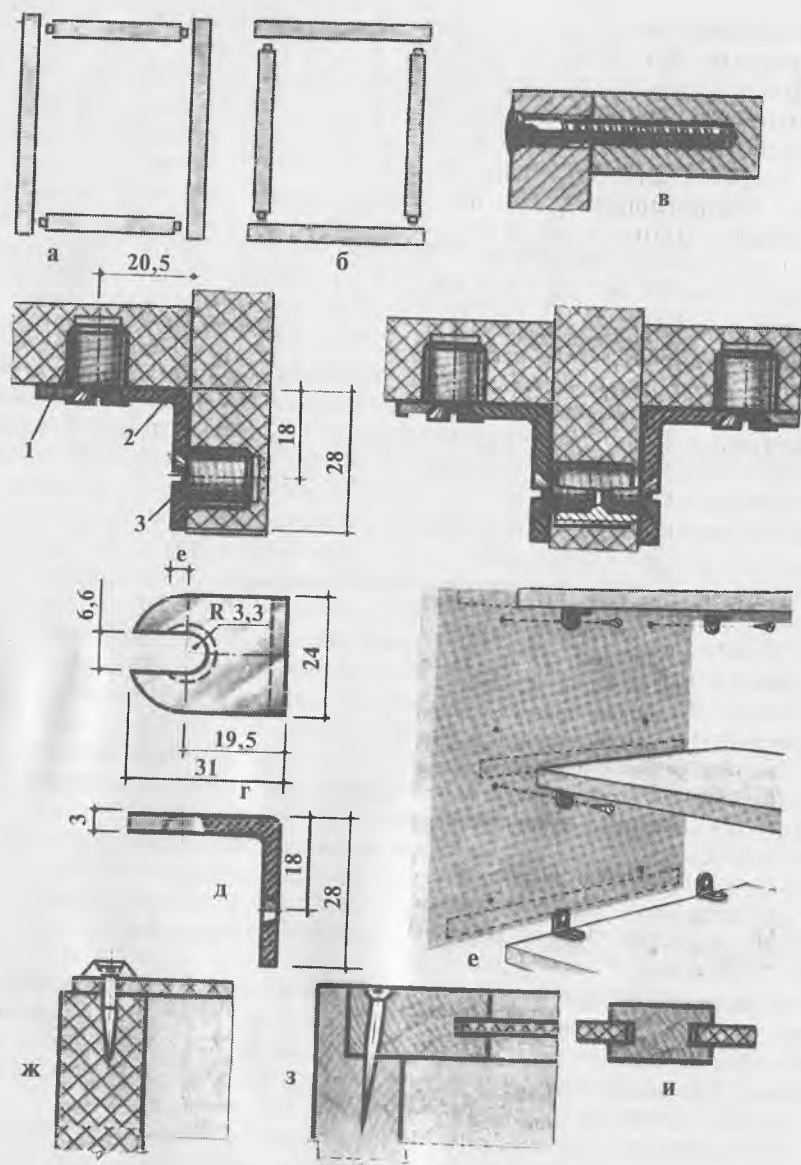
Схемы расположения стенок корпуса и соединения стенок:
